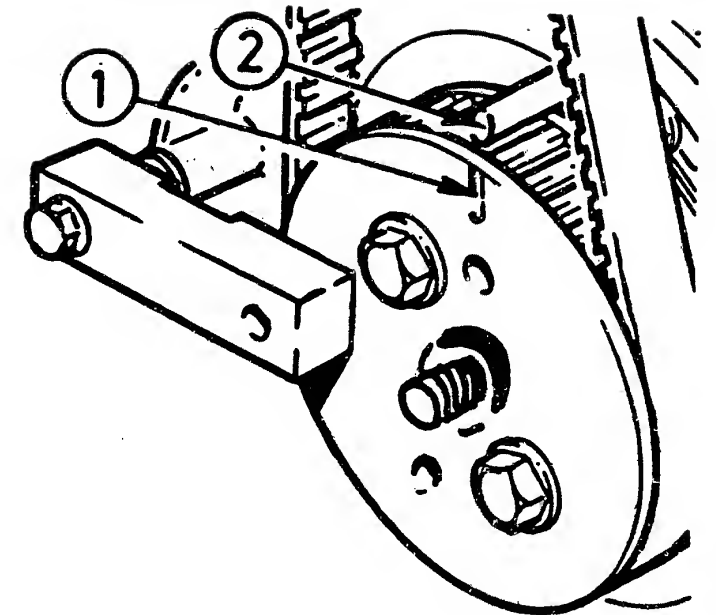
Sichern des Zahnrades bei ausgebauter Diesel-Einspritzpumpe mit dem zum Abdrücken verwendeten Werkzeug.
